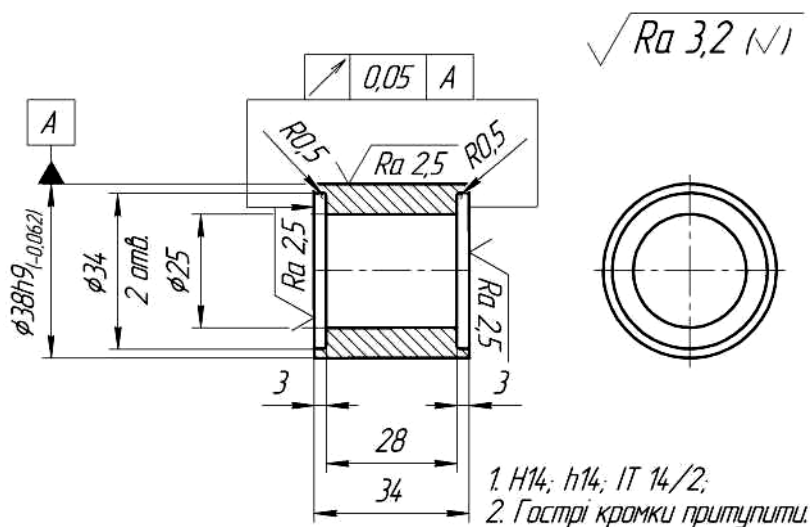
Фрагмент робочого креслення деталі типу «втулка»
